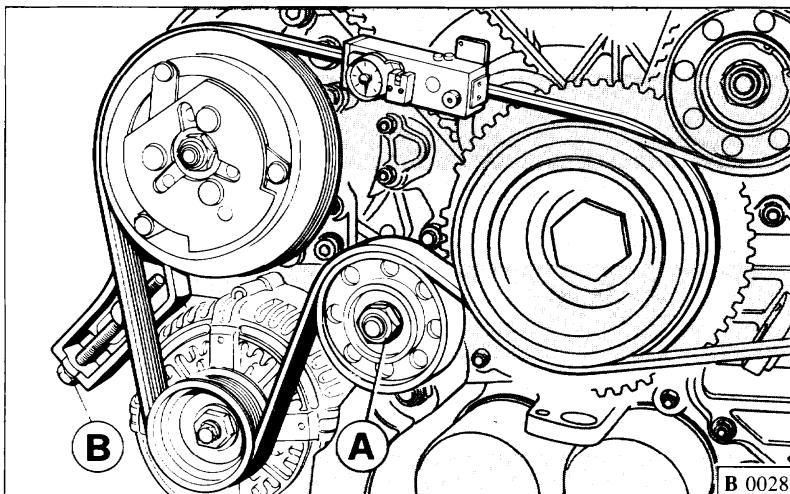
Tensione cinghia compressore A.C. e alternatore.
